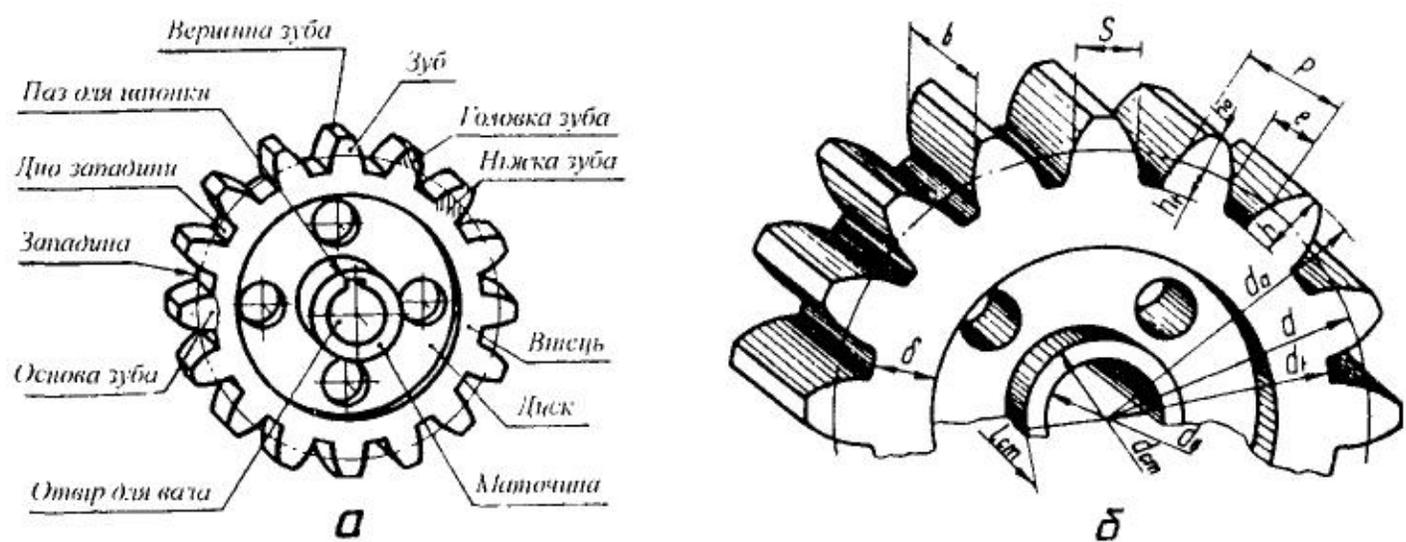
Циліндричне зубчасте колесо: а — загальний вигляд; б — основні параметри.
